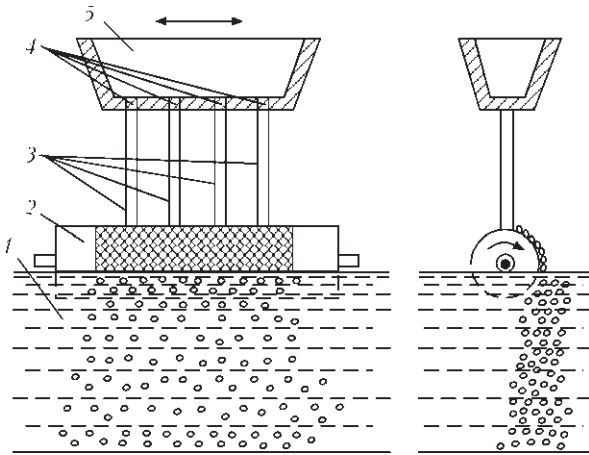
Схема получения дробы механическим дроблением струи жидкого металла: 1 — охлаждающая вода; 2 — распылительный барабан; 3 — струи расплава; 4 — литниковые каналы для истечения расплава; 5 — промежуточный ковш
